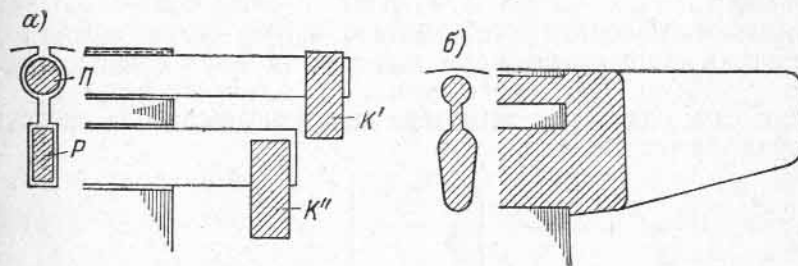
Ротор двухклеточного двигателя: а — с двумя обмотками; б — с заливкой алюминием
